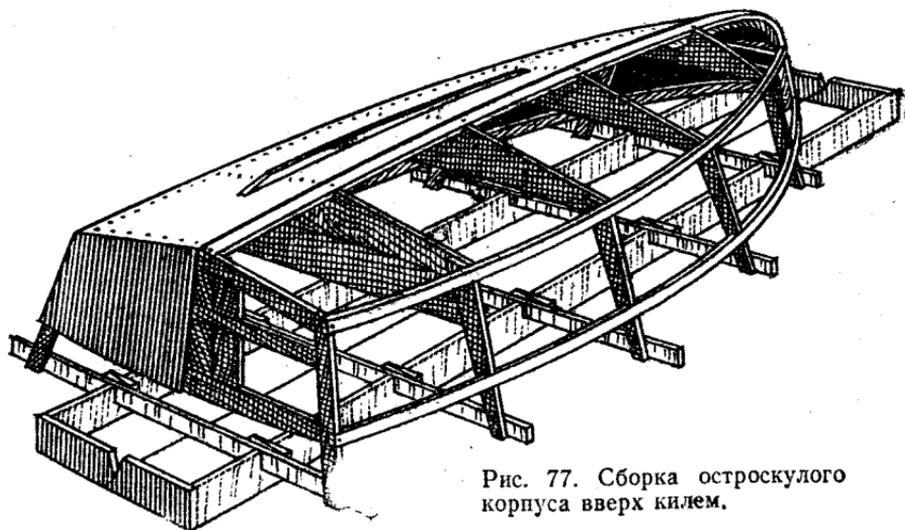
Сборка остроклюлого корпуса вверх килем.
